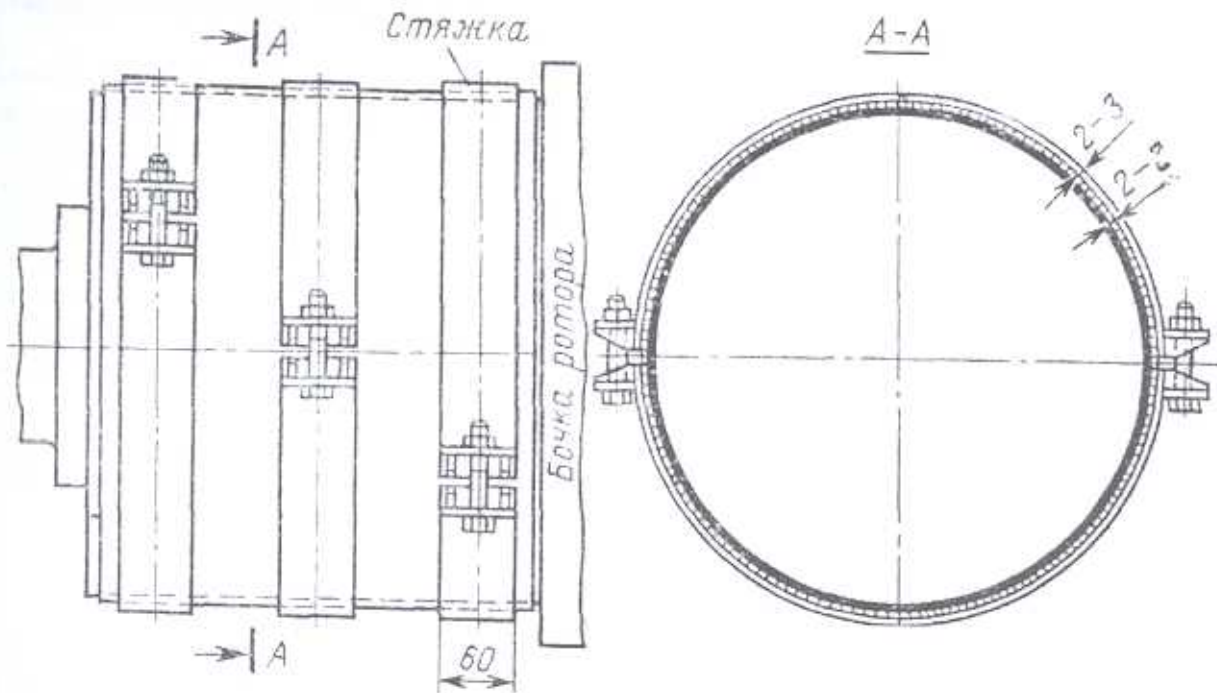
Опрессовка лобовых частей обмотки ротора хомутами
